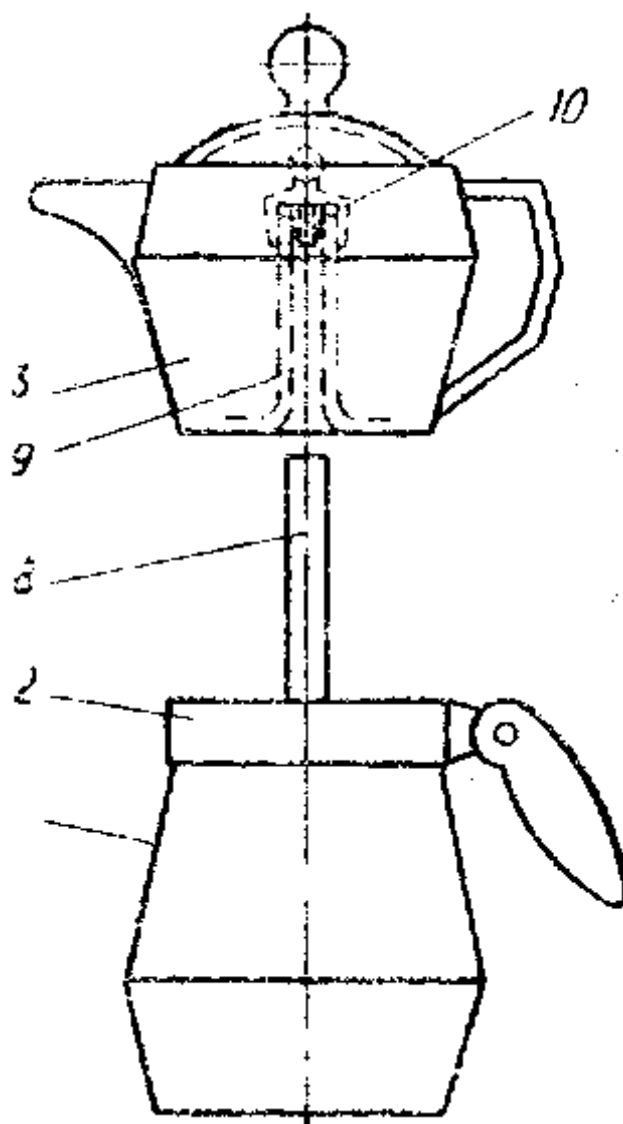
Зовнішній вигляд кавоварки із розділеними частинами
